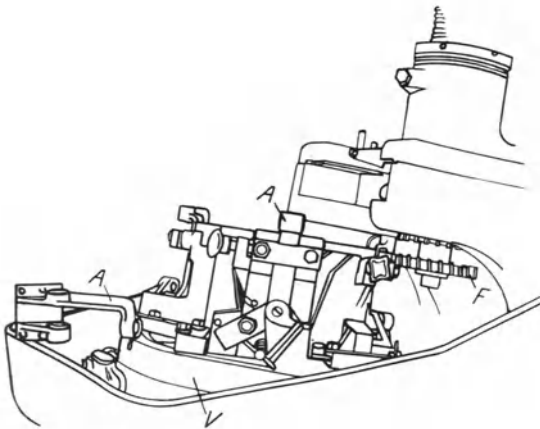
Das Fräsen auf einer 3-Stationen-Vorrichtung.
